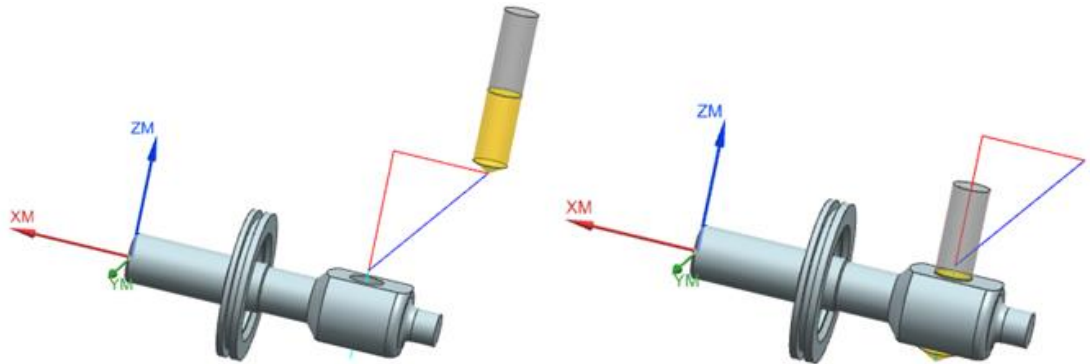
Ескіз обробки для свердильного переходу
